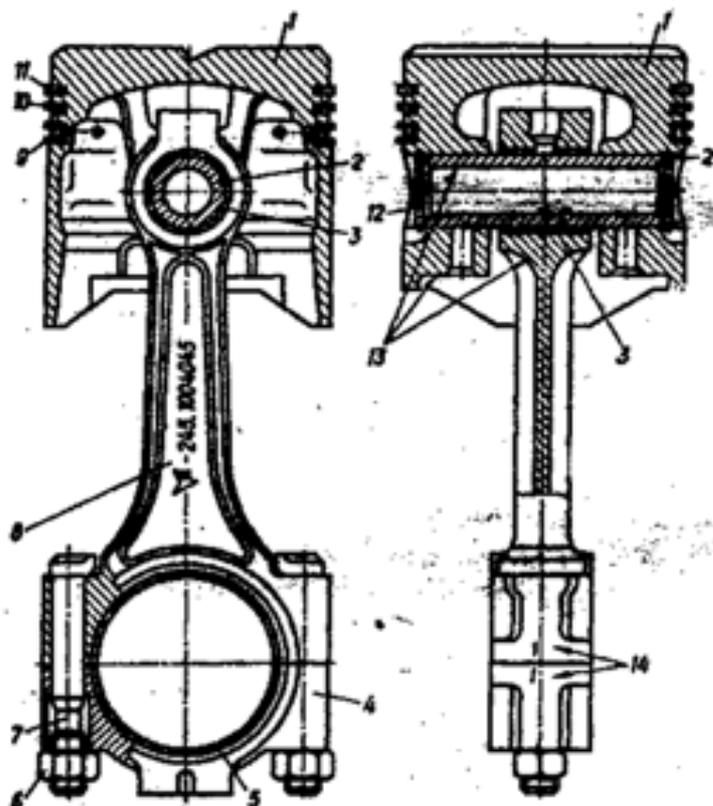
Шатуны с поршнем в сборе: 1 - поршень; 2 - поршневой палец; 3 - втулка шатуна; 4 - крышка шатуна; 5 - вкладыши; 6 - гайка болта крышки шатуна; 7 - болт крышки шатуна; 8 - шатун; 9 - маслоъемное кольцо в сборе; 10 и 11 - нижнее и верхнее компрессионные кольца; 12 - стопорное кольцо; 13 - места цветовой маркировки шатуна, бобышки поршня и поршневого пальца; 14 - клеймо номера цилиндра
